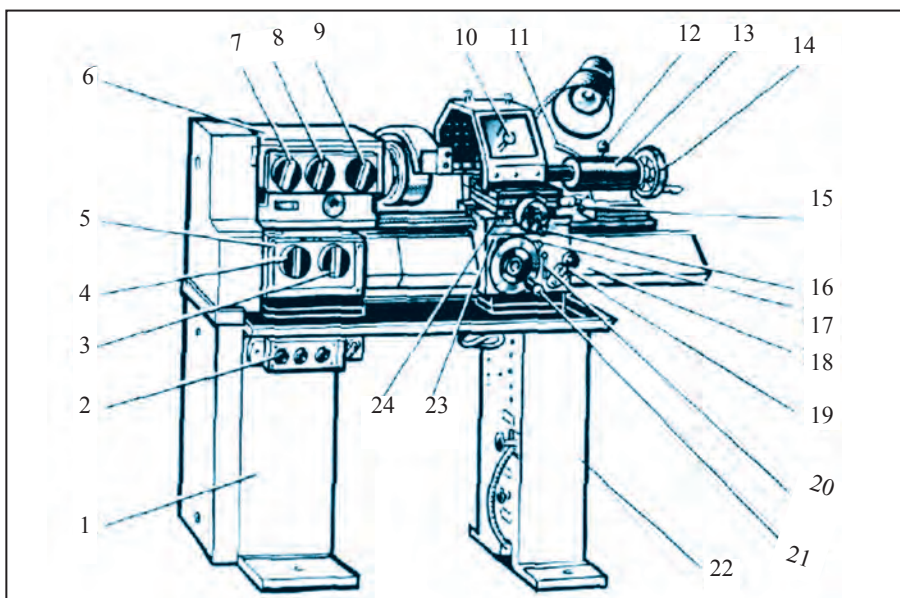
Токарно-винторезный станок ТВ-6: 1 – передняя тумба; 2 – кнопки управления; 3 – рукоятка приведения в действие пускового валика и пускового винта; 4 – рукоятка установки величины передачи и шага резьбы; 5 – ящик приводов; 6 – передняя бабка; 7 – рукоятка изменения направления привода; 8 и 9 – рукоятка установки частоты вращения шпинделя; 10 – рукоятка установки головки резца; 11 – рукоятка установки пиноля задней бабки; 12 – рукоятка установки задней бабки на направляющую станины; 13 – задняя бабка; 14 – рукоятка передвигания пиноля задней бабки; 15 – рукоятка передвигания верхних салазок суппорта вручную; 16 – рукоятка передвигания поперечных салазок; 17 – рукоятка приведения в действие реечной шестерни; 18 – станина; 19 – рукоятка приведения в действие гайки пускового винта; 20 – рукоятка приведения в действие поперечного механического привода; 21 – рукоятка продольного ручного привода; 22 – задняя тумба; 23 – фартук; 24 – суппорт.
